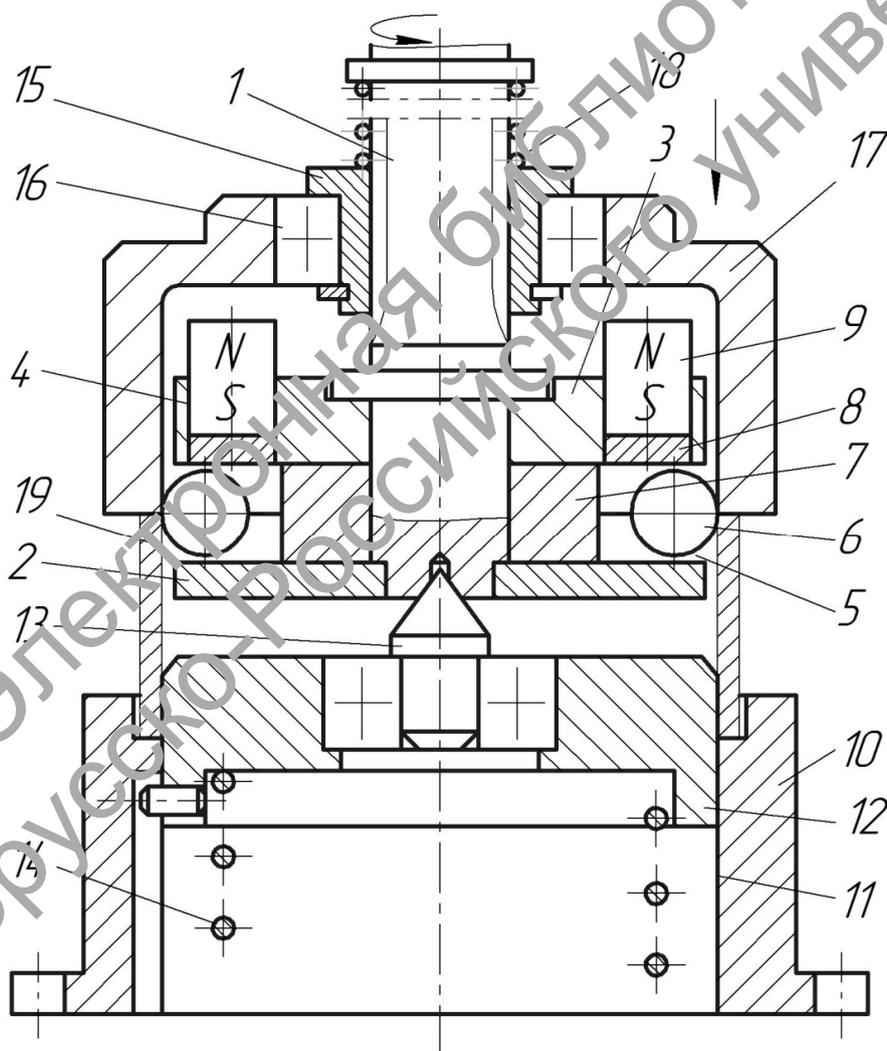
Инструмент для совмещенной упрочняющей обработки нежестких втулок в условиях серийного производства: 1 – оправка; 2 – шайба; 3 – диск; 4 – аксиальные отверстия; 5 – кольцевая камера; 6 – деформирующие шары; 7 – проставочное кольцо; 8 – цилиндрические магнитопроводы; 9 – цилиндрические постоянные магниты; 10 – корпус; 11 – центральное отверстие; 12 – шток; 13 – вращающийся центр; 14 – пружина возврата; 15 – гильза; 16 – подшипниковая опора; 17 – цилиндрический кондуктор; 18 – пружина; 19 – упрочняемая втулка
